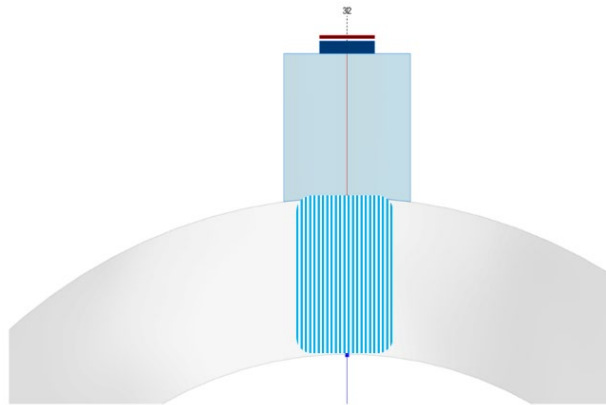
Inspección por haz longitudinal con zapata de haz recto
